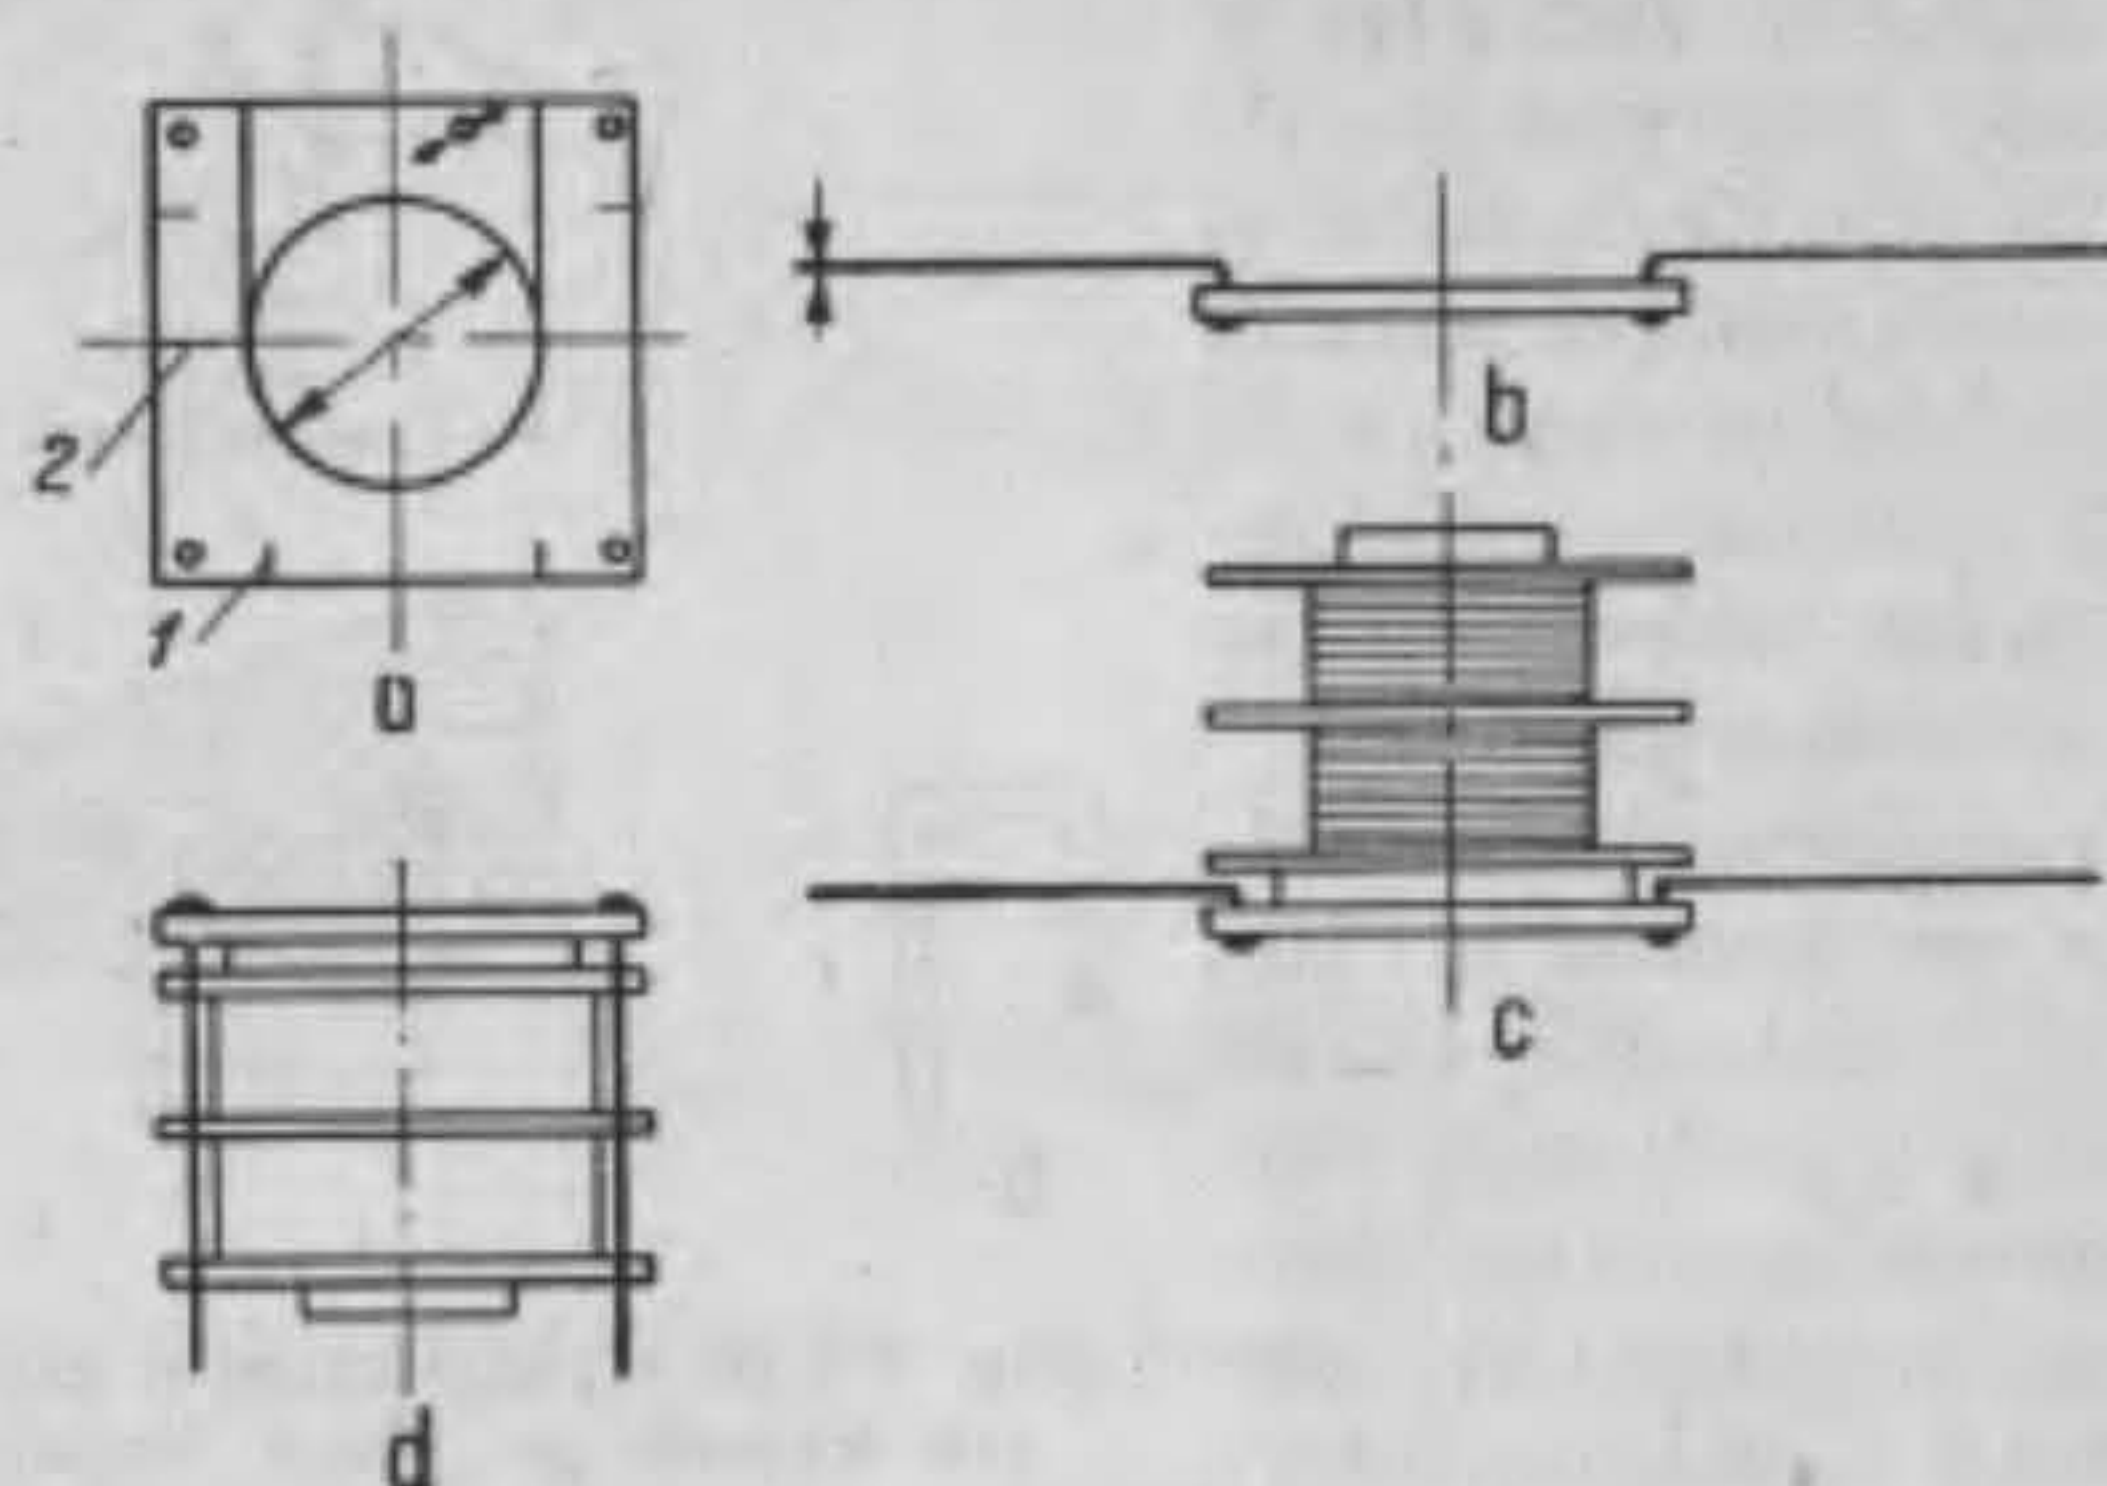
Construcția și fixarea unei bobine pe placa imprimată :
